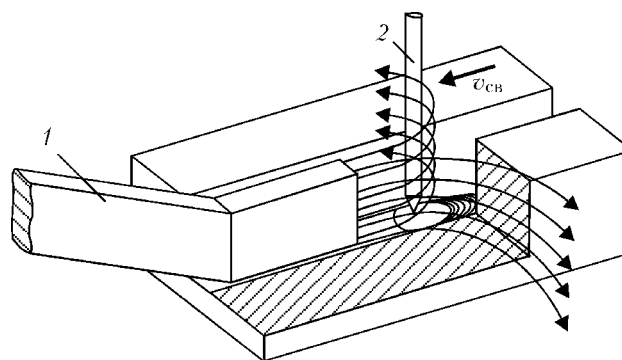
Схема сварки в узкий зазор магнитоуправляемой дугой: 1 — магнитопровод; 2 — электрод
